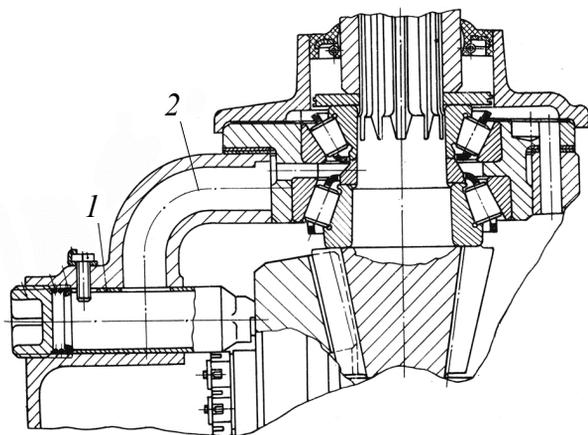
Схема подачи смазочного материала к подшипникам ведущей шестерни автомобиля ГАЗ-66
